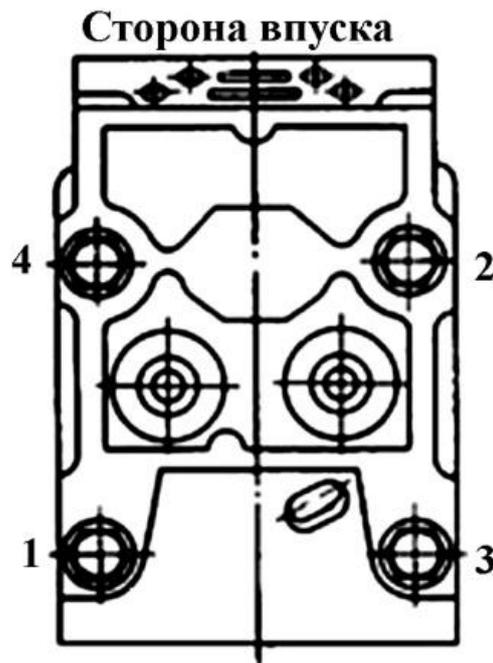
Порядок затяжки болтов крепления головки блока цилиндров двигателя КамАЗ-740
